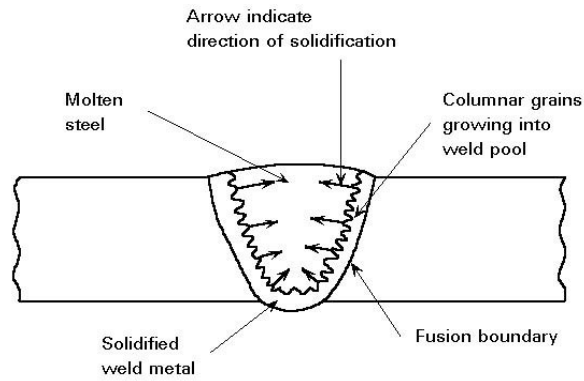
Solidification de métal de la soudure.
